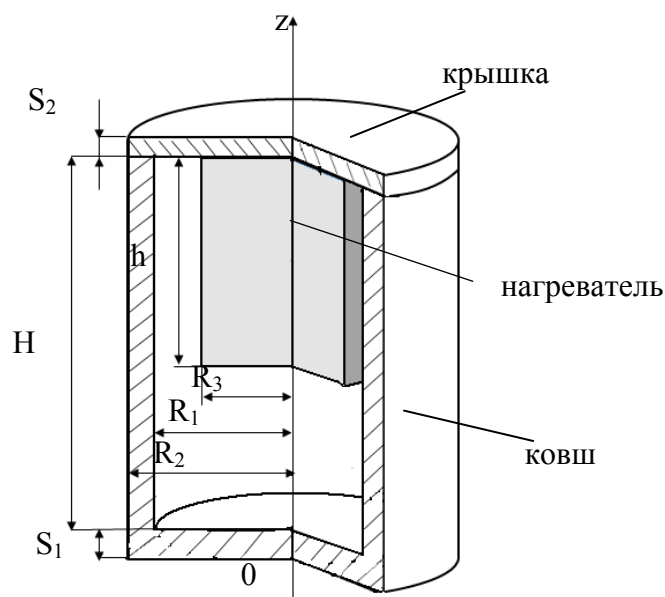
Схема сталеразливочного ковша с электрическим нагревателем
